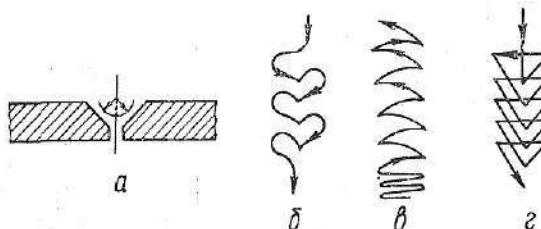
Движение электрода при сварке стыкового шва с V-образной разделкой кромок:
